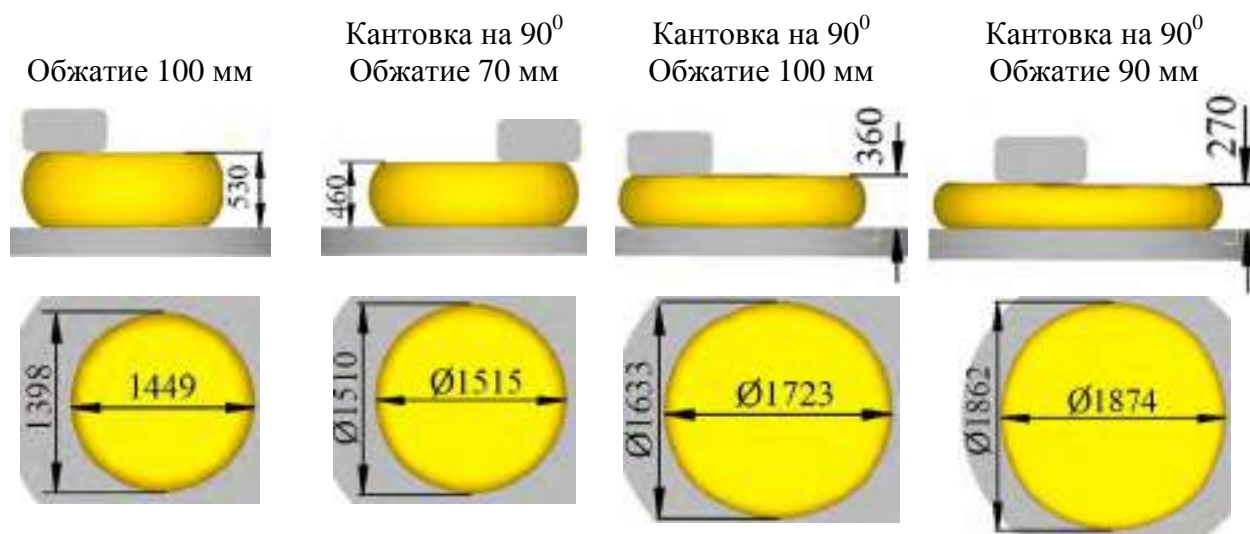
Формоизменение заготовки в процессе разгонки заготовки узким бойком
